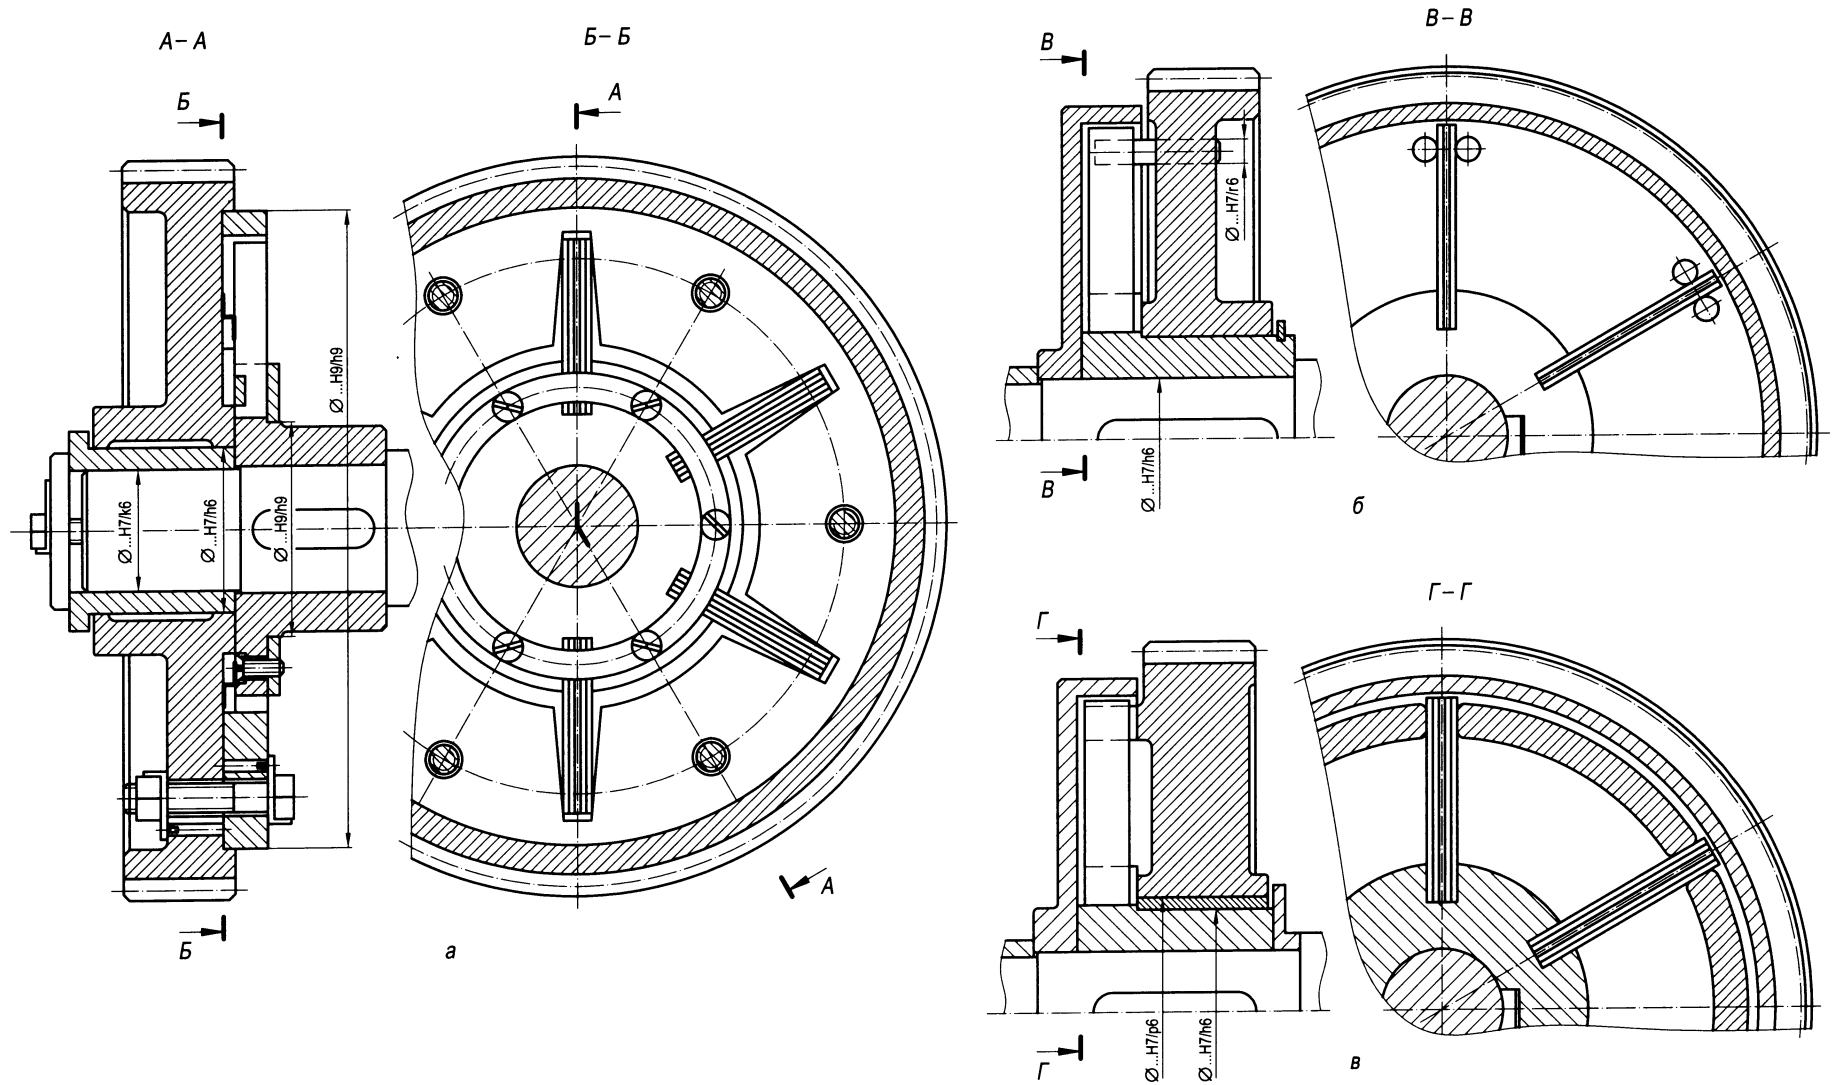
Эскизы зубчатых колес быстроходной передачи с пакетами пластин, размещенными в радиальном направлении
